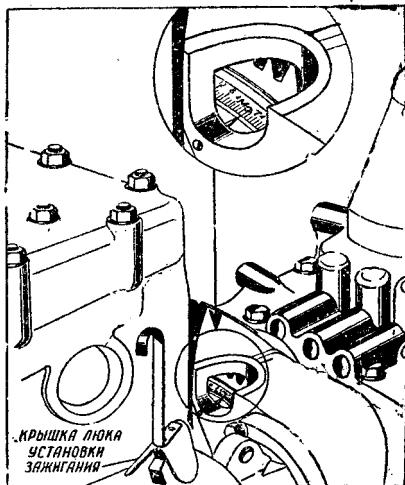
Окно для установки коленчатого вала в положении верхней мертвоточки.
